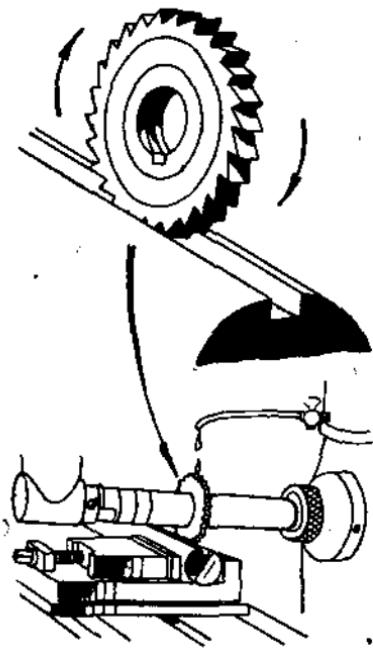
Изготовление шпоночного паза на валу посредством фрезерования.
